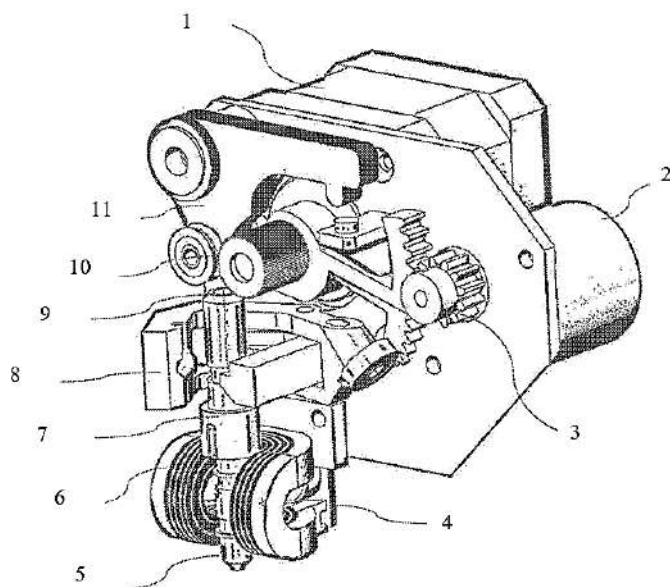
Устройство для захвата сопла, загруженного различными компонентами: 1 – шаговый двигатель; 2 – редуктор; 3 – корпус; 4 – съёмный элемент; 5 – съёмное сопло; 6 – нагреватель; 7 – термобарьер; 8 – фиксатор; 9 – штуцер для загрузки прутка пластика; 10 – проталкивающий вал; 11 – зажим
